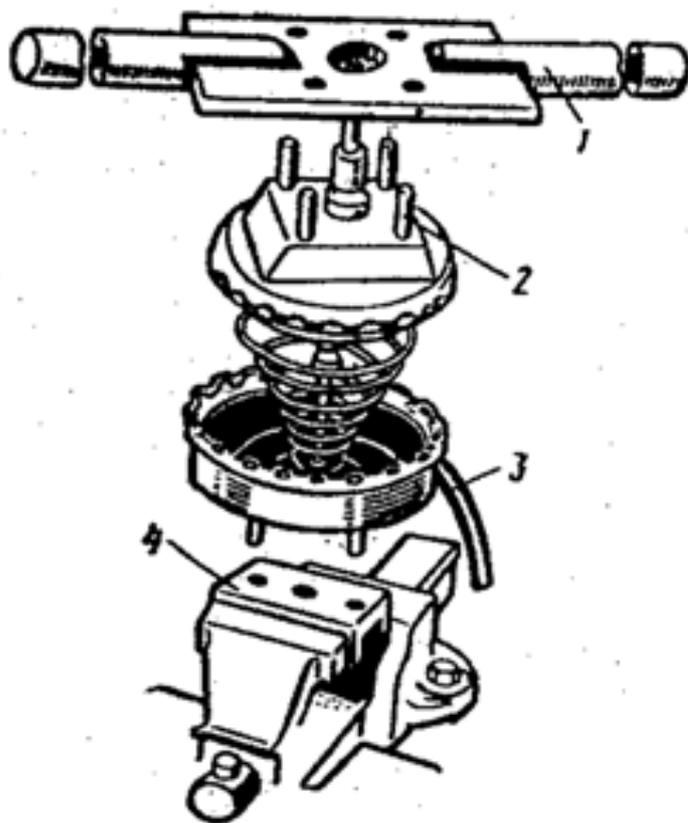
Схема разборки вакуумного усилителя: 1 - рычаг; 2 - болт; 3 - шланг; 4 - планка.
